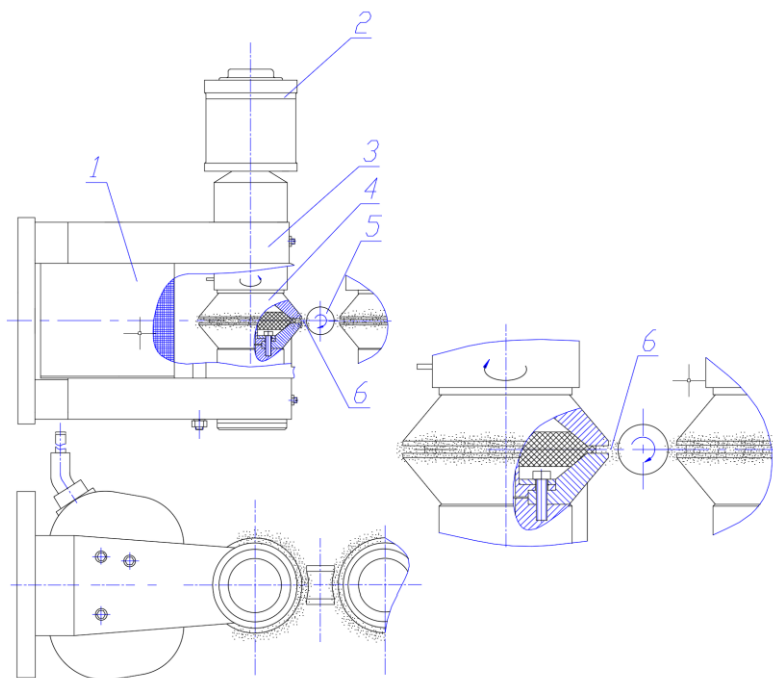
Схема исследовательской установки: индуктор (1); электродвигатель (2); магнитопровод (3); полюсный наконечник (4); обрабатываемая деталь (5); ферромагнитный порошок (6)
